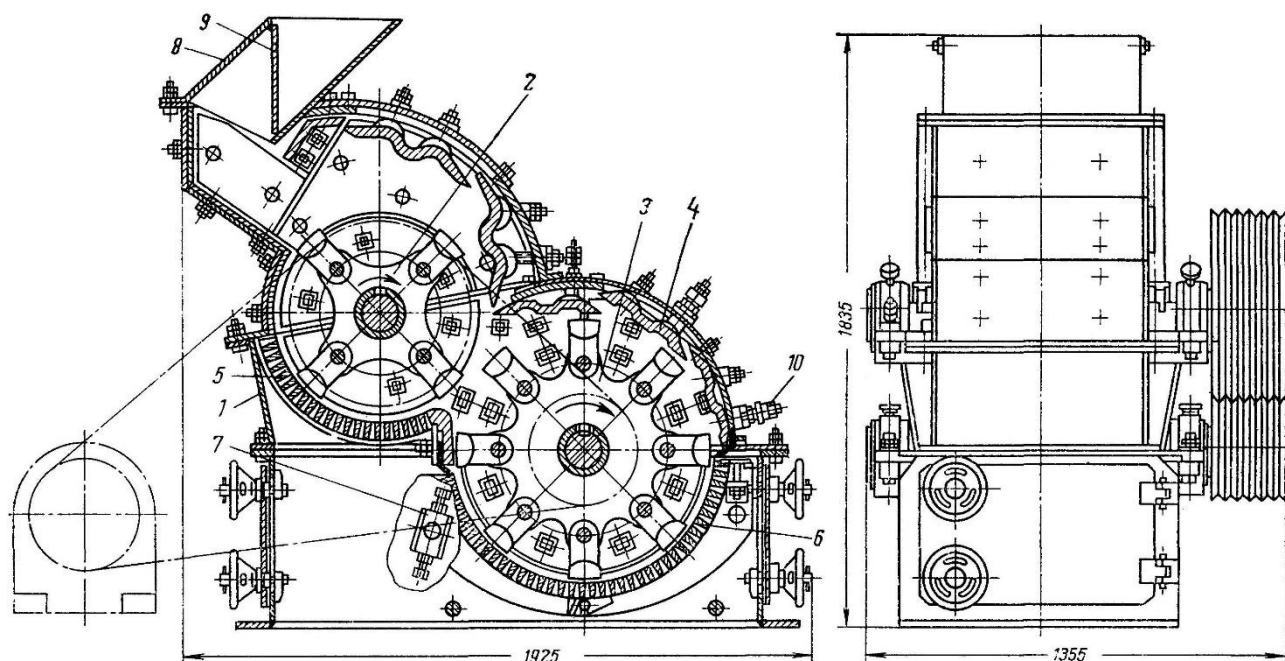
Молоткова двороторна дробарка з послідовним розташуванням роторів [16, 17, 21]: 1 - корпус; 2 - ротор верхній; 3 - ротор нижній; 4 - відбійні плити; 5 - верхня колосникова решітка; 6 - нижня колосникова решітка; 7 - механізм регулювання колосникових решіток; 8 - завантажувальна лійка; 9 - заслінка; 10 - механізм регулювання відбійних плит
